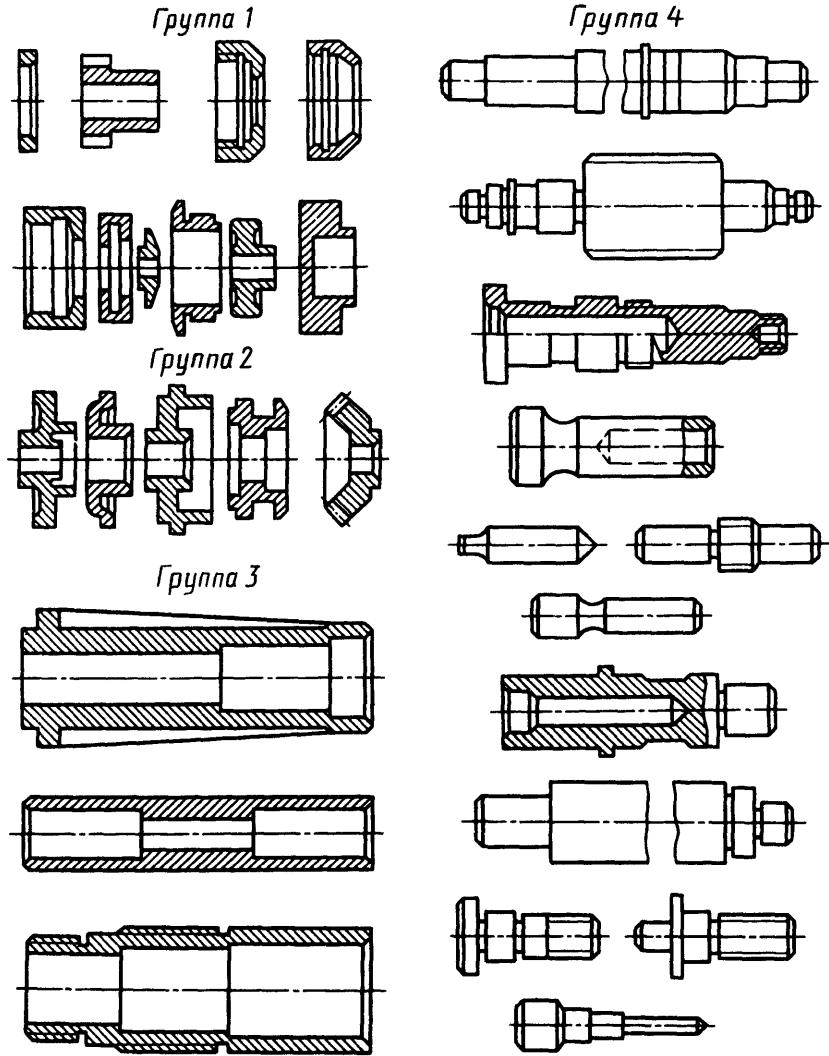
Группы заготовок, обрабатываемые на токарном станке без переналадки
